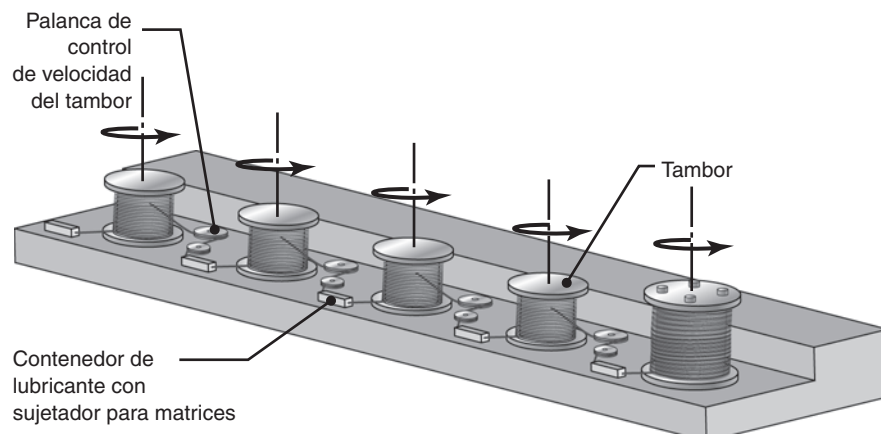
Ilustración de estirado de alambre de etapas múltiples, utilizadas comúnmente para producir alambre de cobre para cableado eléctrico. *Fuente:* H. Auerswald.
